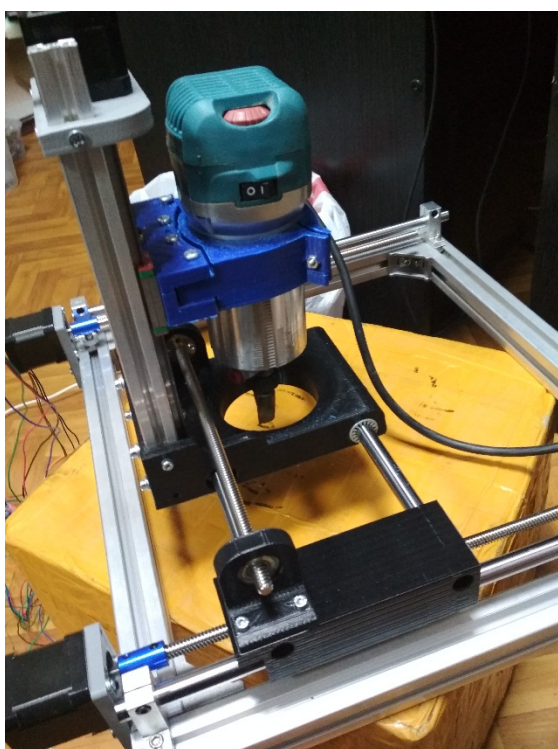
Собранный прототип платформы с установленным фрезером для проведения проверок
